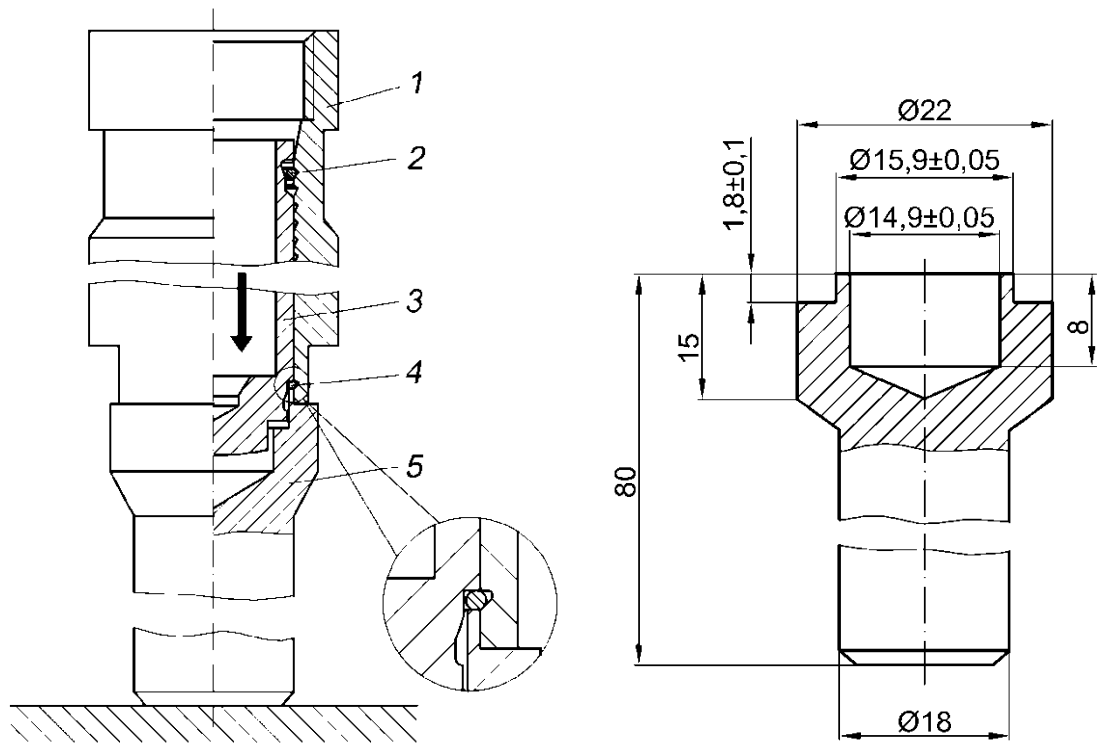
Сборка гидронатяжителя, применяемого без адаптера, с помощью оправки:
